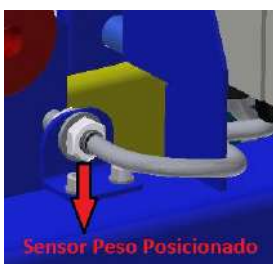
Sensor Posicionado (Figura Ilustrativa)
